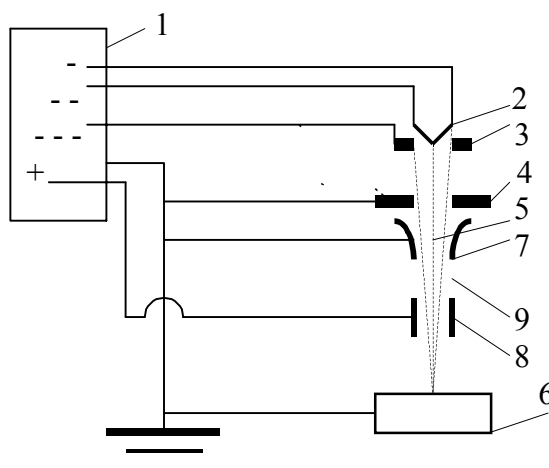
Общий вид устройства для сварки тугоплавких материалов.
